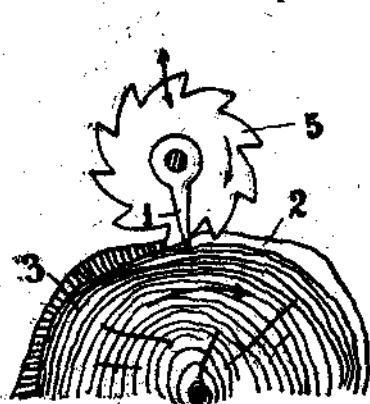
Фрезерное приспособление с подрезающим ножом.
